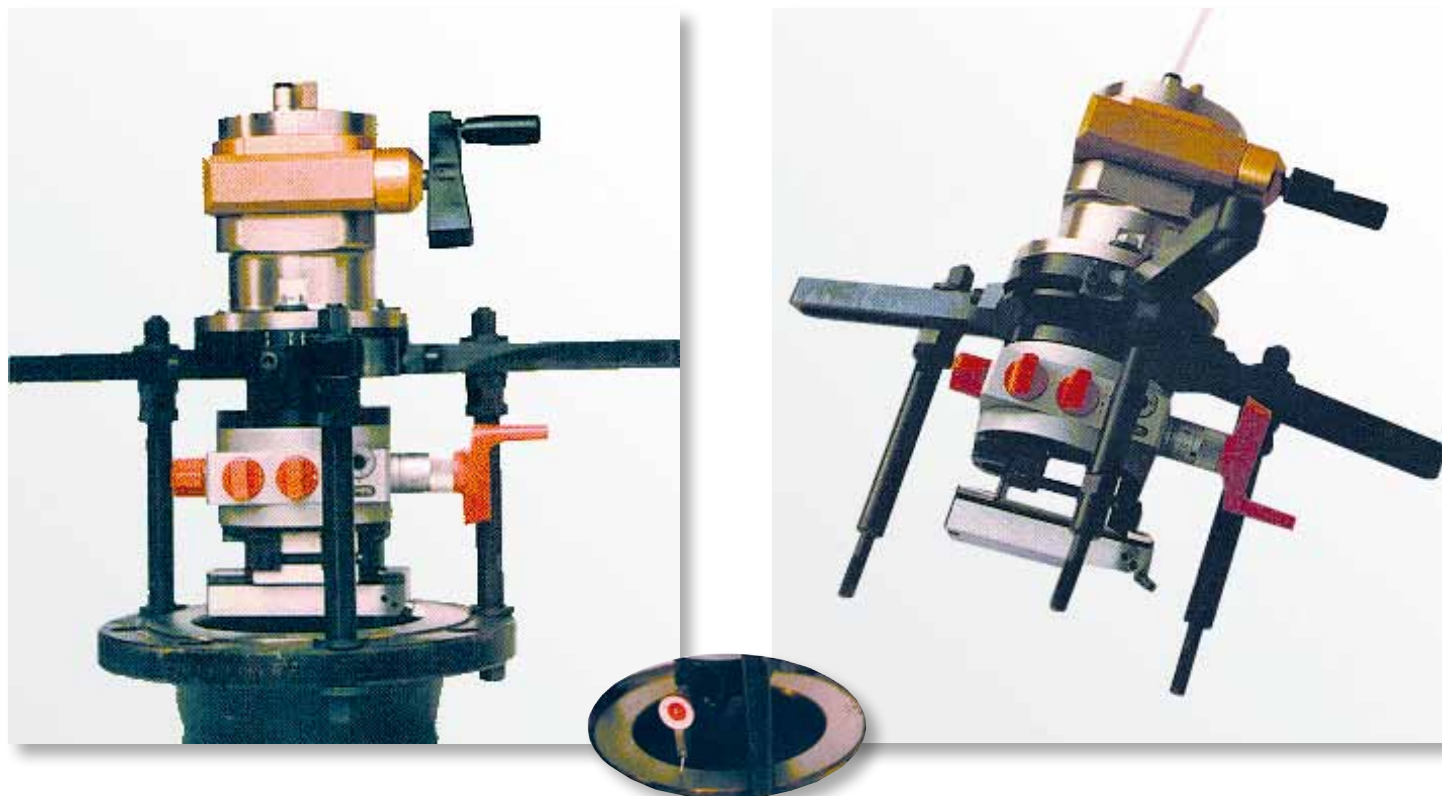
E - External bevel working tool - Utensile per smusso esterno C.n. 106403
